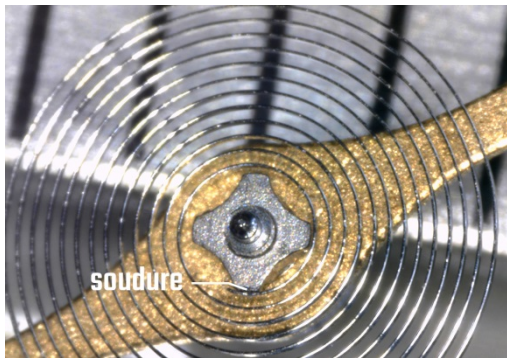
Schweißen der Spirale auf die Spiralrolle
